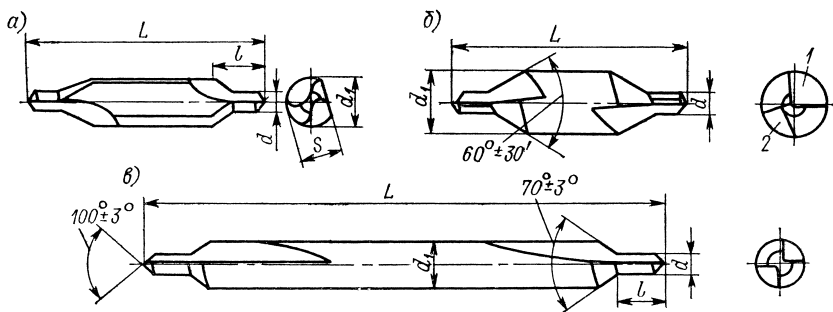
Сверла специальные комбинированные: а — с лыской; б — с разделением потока стружки; в — для обработки плат печатного монтажа
